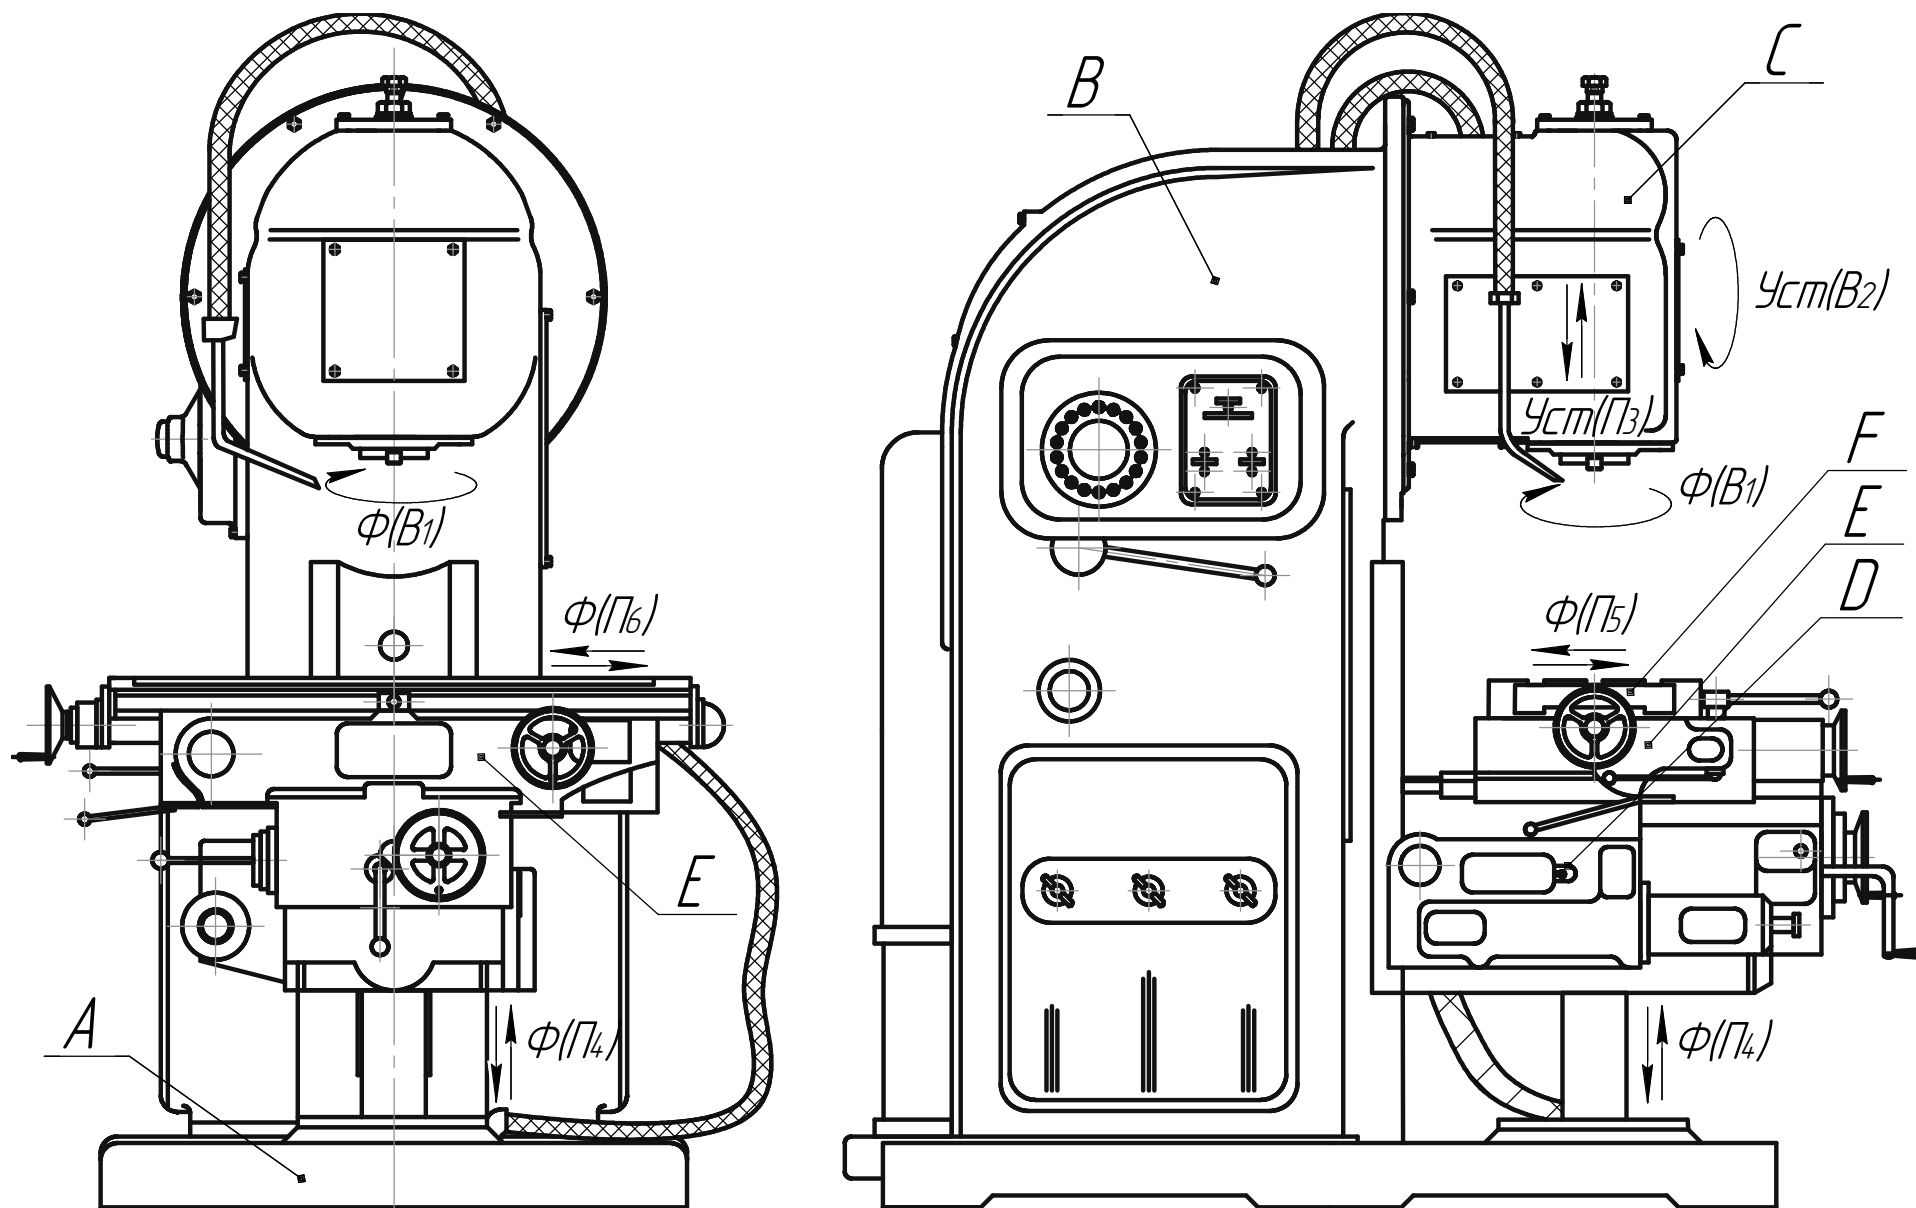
Загальний вигляд консольного вертикально-фрезерного верстата 6С12Ц
